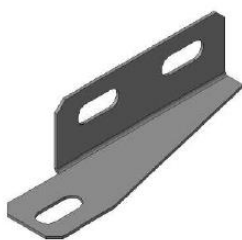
Соединитель поворотный лотка лестничного (1,2) ПжТехКабель
